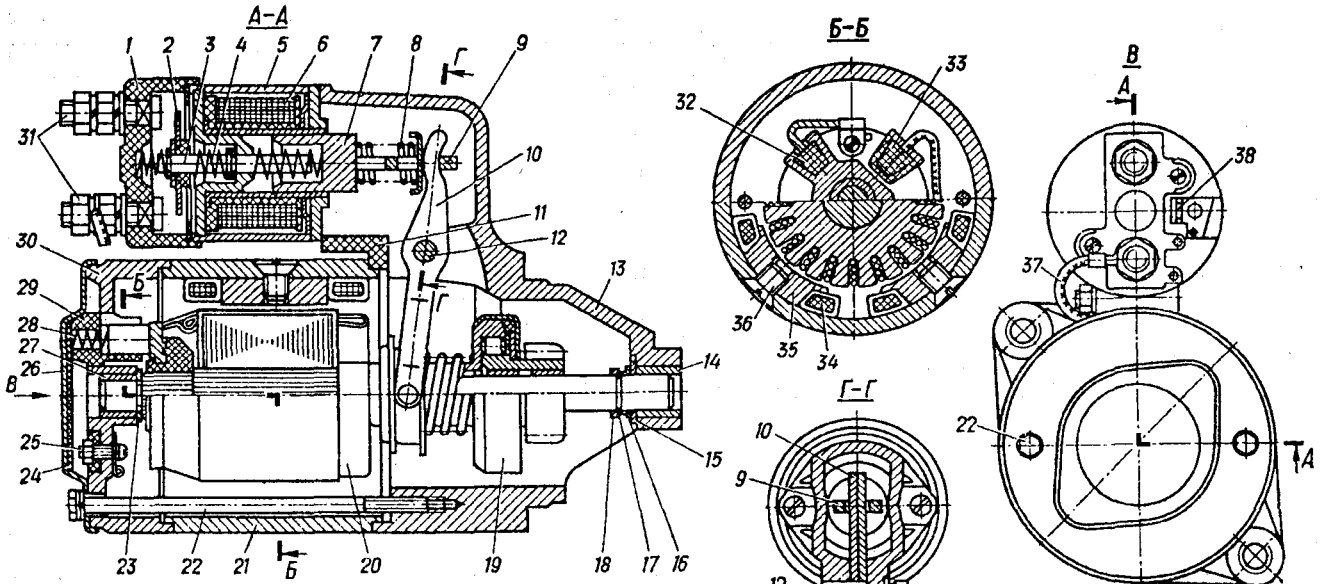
Стартер: 1 – крышка реле; 2 – контактный диск; 3 – шток реле в сборе; 4 – пружина контактного диска; 5 – корпус реле; 6 – обмотка реле; 7 – якорь реле; 8 – пружина якоря; 9 – серьга якоря; 10 – рычаг; 11 – прокладка; 12 – ось рычага; 13 – крышка со стороны привода; 14, 27 – втулки якоря; 15, 16, 23 – шайбы упорные; 17 – кольцо стопорное; 18 – кольцо упорное; 19 – роликовая муфта с шестерней; 20 – якорь в сборе; 21 – статор; 22 – стяжной болт; 24 – прокладка изоляционная; 25 – винт; 26 – колпак; 28 – пружина щетки; 29 – пластмассовый щеткодержатель; 30 – крышка со стороны коллектора; 31 – контактные болты тягового реле; 32 – щетка неизолированная; 33 – щетка изолированная; 34 – катушка возбуждения; 35 – полюс; 36 – полюсный винт; 37 – вывод от катушки возбуждения; 38 – вывод обмоток реле (штеккер внутренний)
